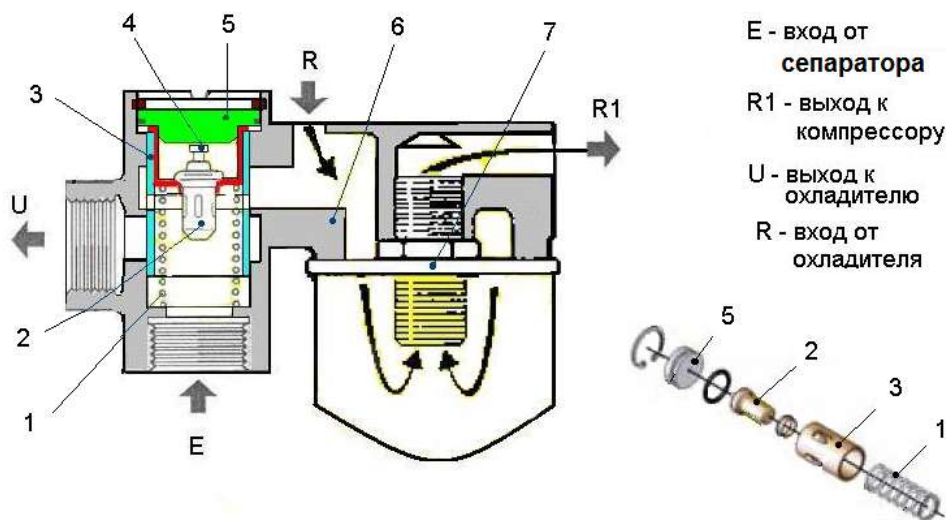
Схема потоков масла через клапан – термостат: 1 – пружина 2 - термозлемент; 3 - стакан; 4 – шток; 5 – заглушка; 6 – корпус гидроплиты; 7 – фильтр масляный.
